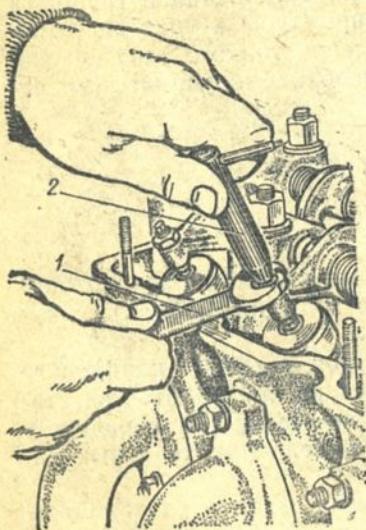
Регулировка зазора между торцами наконечника и стержня клапана:
